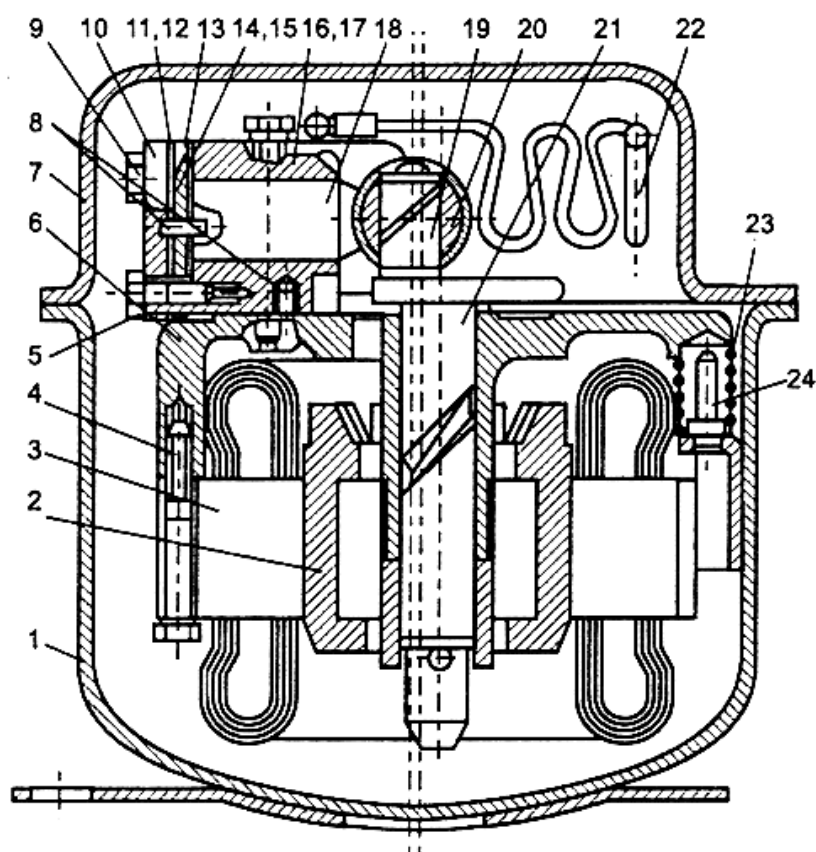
Кулісний мотор-компресор: 1 – кожух у зборі; 2 – ротор; 3 – статор; 4, 5, 9 – гвинти; 6 – корпус компресора; 8 – штифти; 10 – головка циліндра; 11 – прокладка клапана нагнітання; 12 – нагрівальний клапан; 13 – сідло клапанів; 14 – всмоктувальний клапан; 15 – прокладка всмоктувального клапана; 16, 17 – циліндри; 18 – поршень; 19 – обойма; 20 – повзун; 21 – вал; 22 – трубка; 23 – буферна пружина; 24 – шпилька
